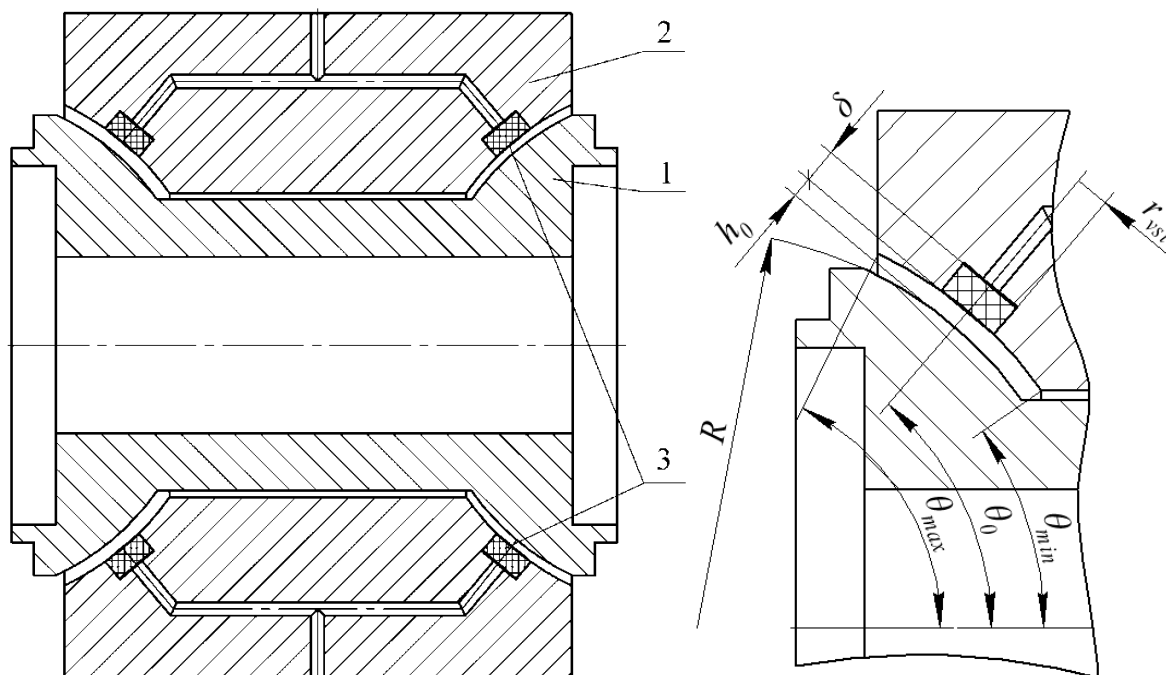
а - разрез шпиндельного узла; б – основные размеры
